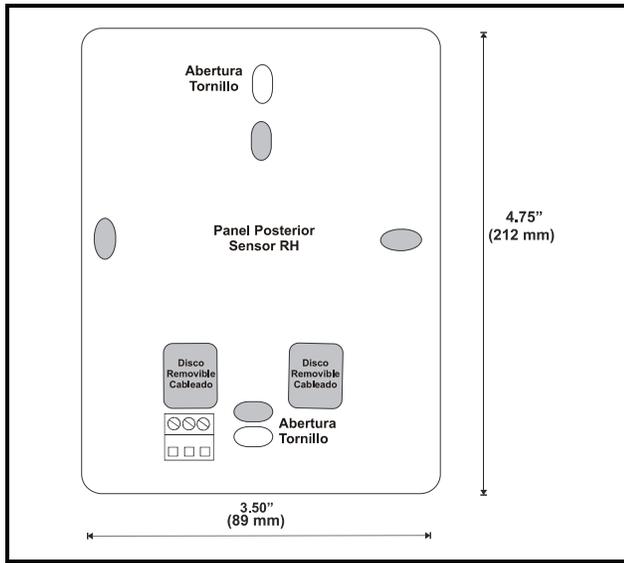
Dimensiones de Montaje del RH de Interior
